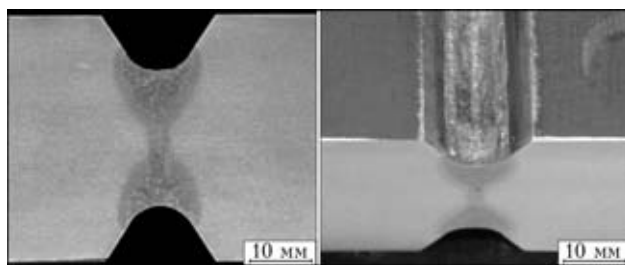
Макрошлиф сварных соединений, полученных на пластинах стали шириной 38 мм двухсторонней односторонней сваркой с разделкой кромок под углом 70°
